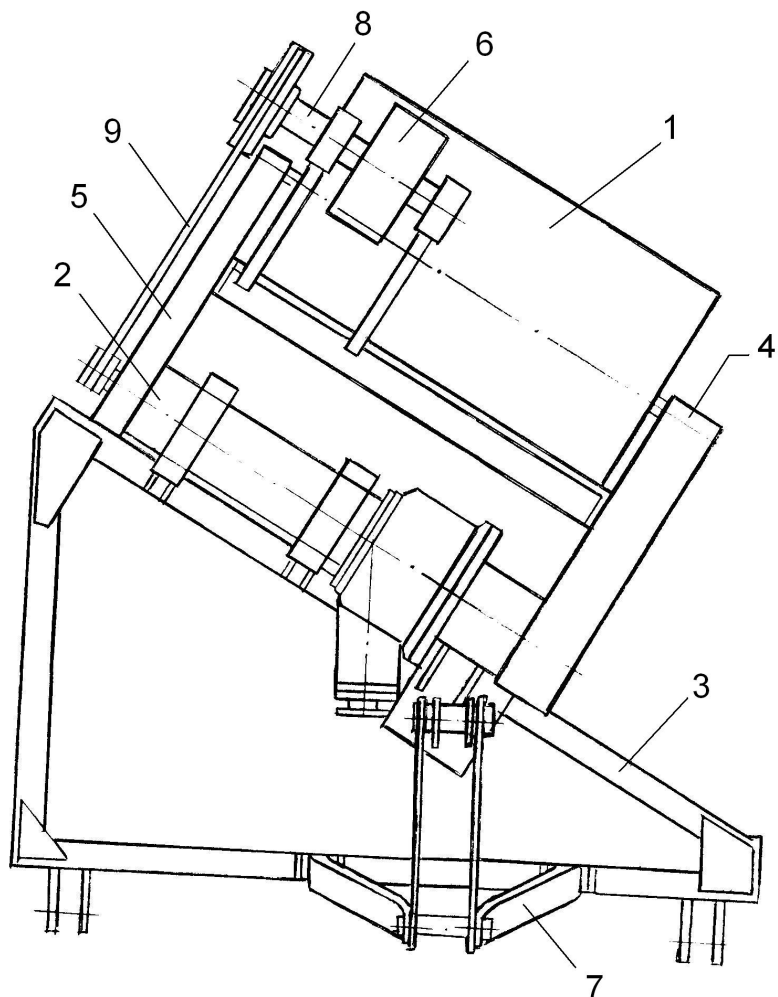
Схема щеточного покровосдирателя (вид сверху):
